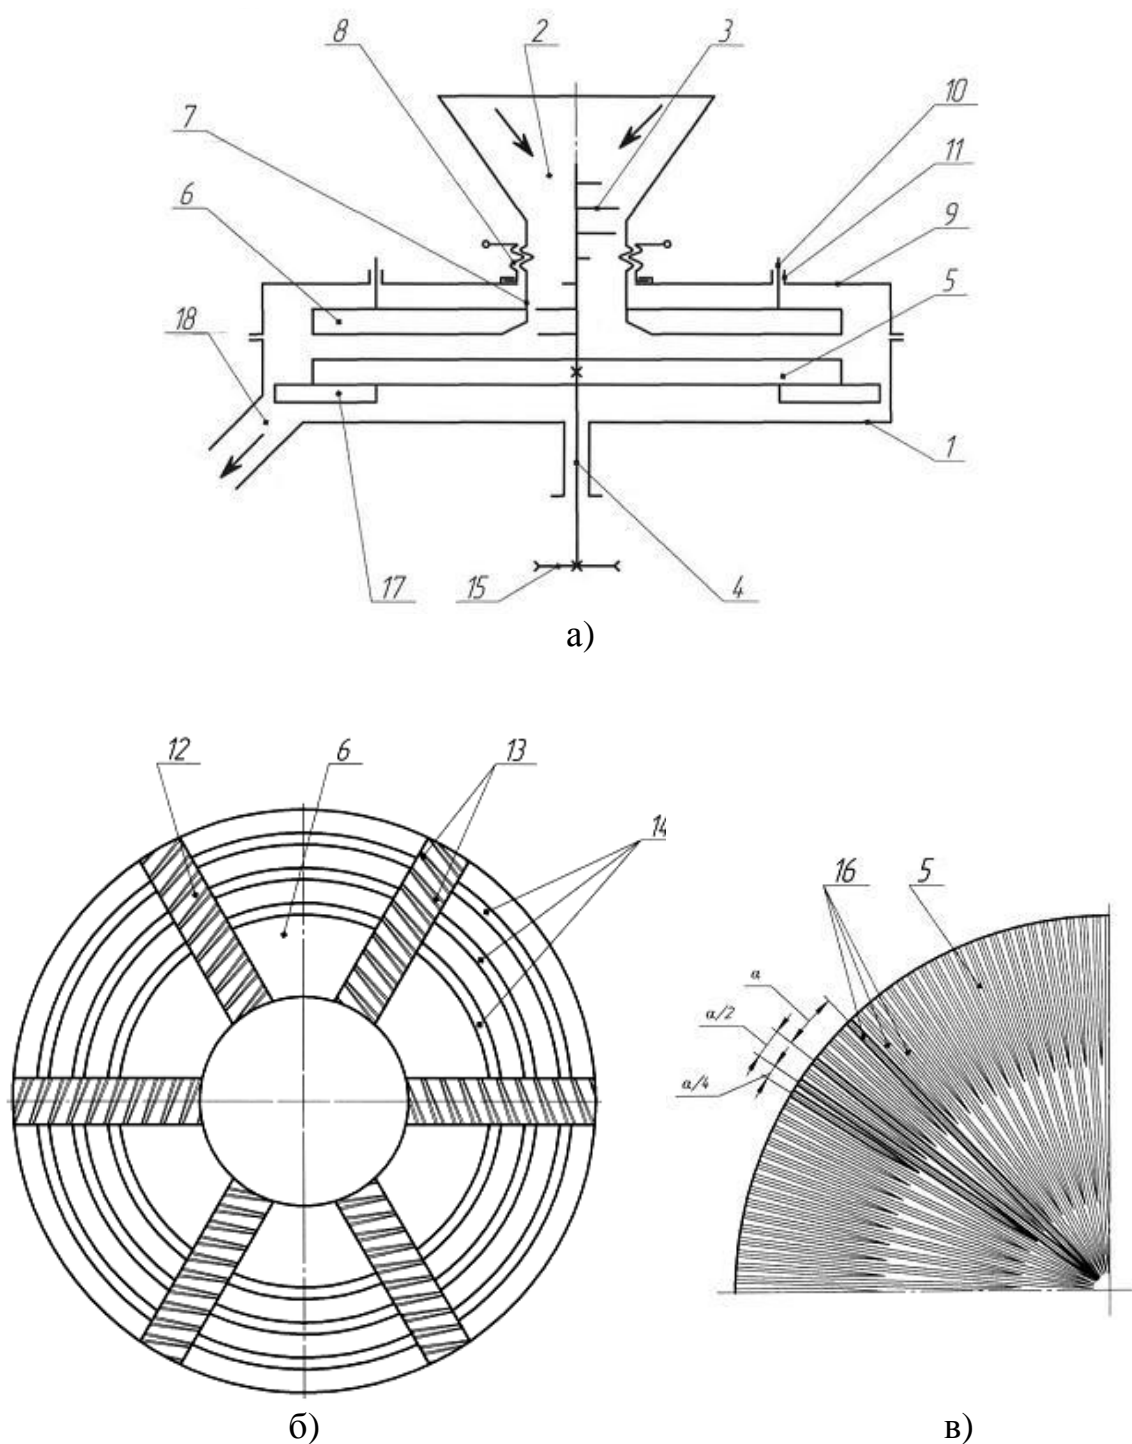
Конструктивна схема: а – терковий пристрій; б – нерухомий диск; в – рухомий терковий диск; 1 – корпус; 2 – завантажувальний канал; 3 – живильник-перегортач; 4 – вал; 5 – рухомий терковий диск; 6 – нерухомий диск; 7 – стакан; 8 – різьбова втулка; 9 – кришка; 10 – штифт; 11 – направляючий отвір; 12 – біла; 13 – риф; 14 – кільцевий виступ; 15 – клинопасова передача; 16 – радіальний паз; 17 – лопатка; 18 – вивантажувальний канал
